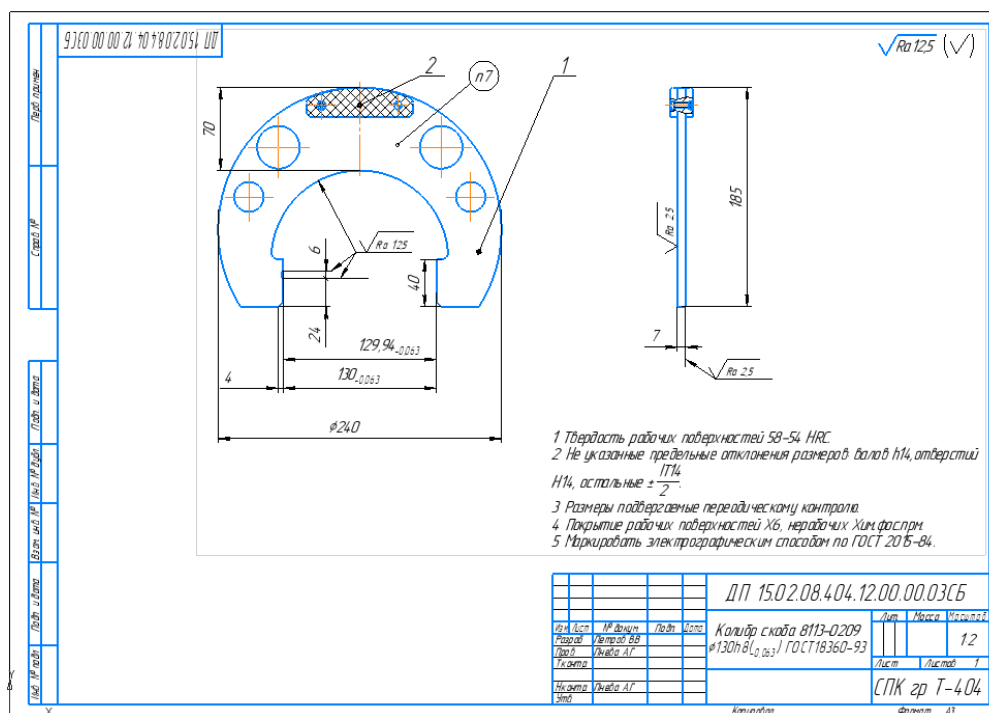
Образец сборочного чертежа измерительного инструмента
